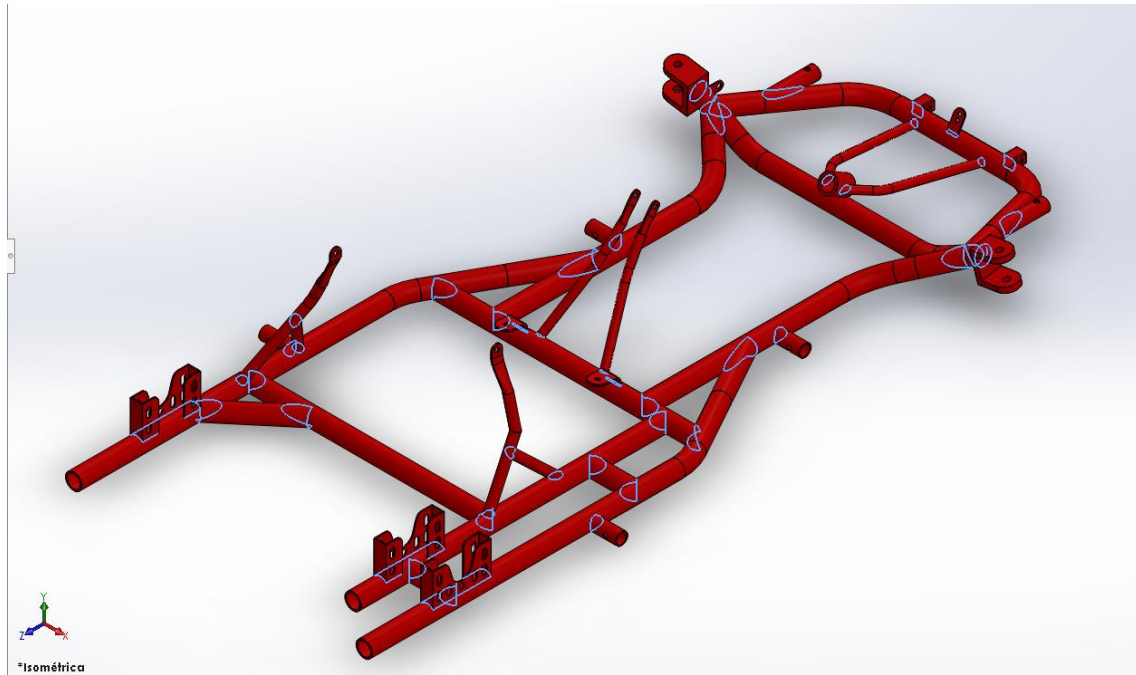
conjunto de cordones de soldadura. Fuente: propia.
